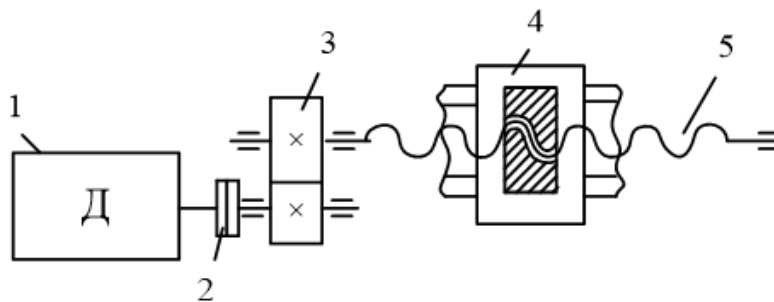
Кінематична схема приводу подачі токарного верстату
